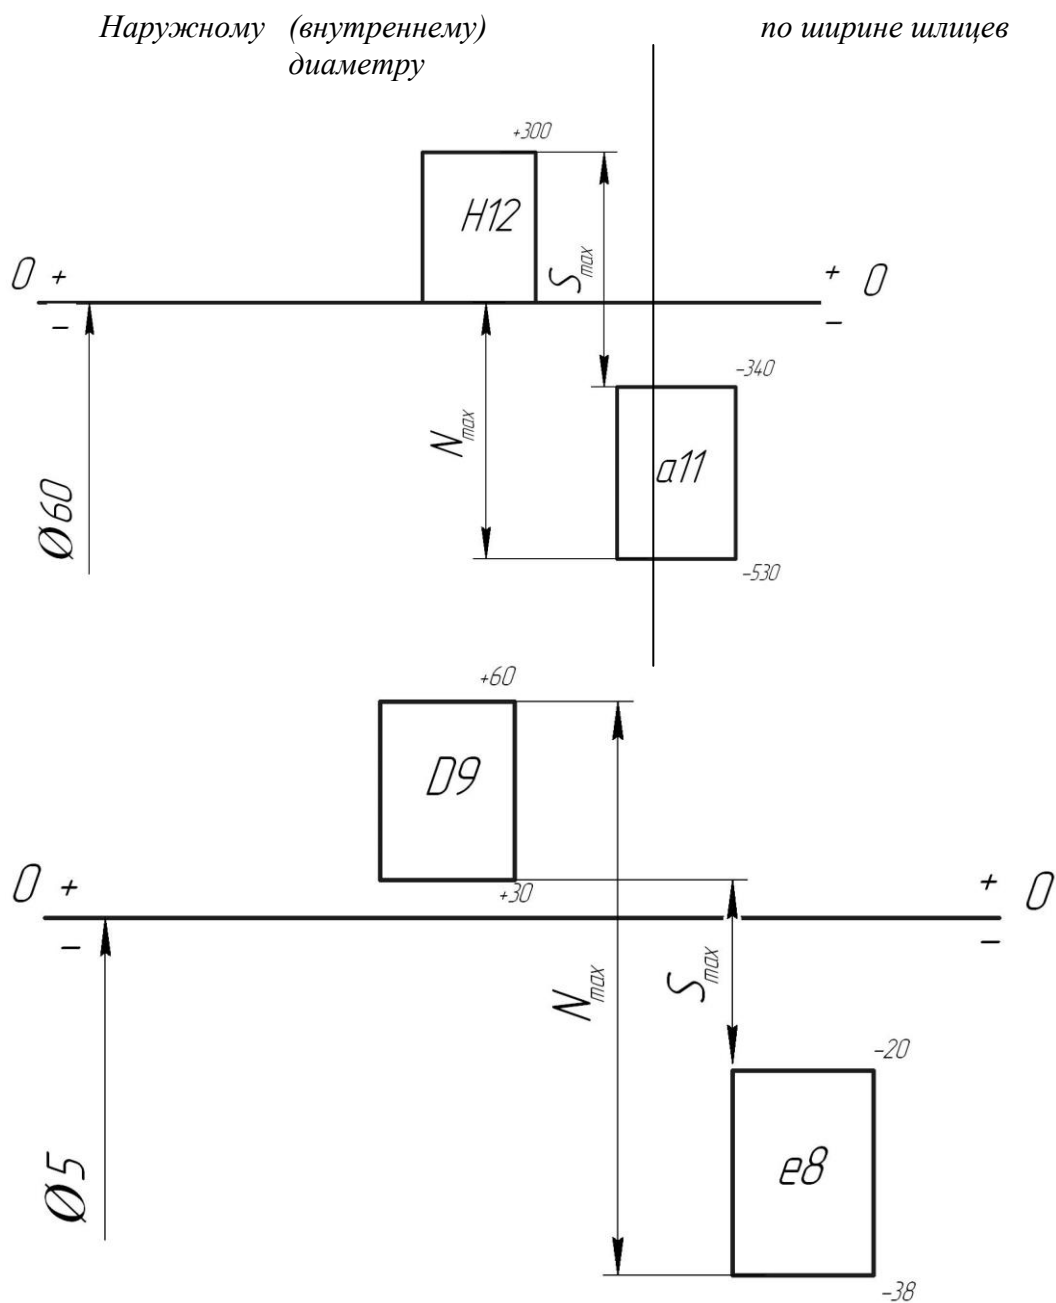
Схемы полей допусков деталей соединения по наружному (внутреннему) диаметру и ширине шлиц.
